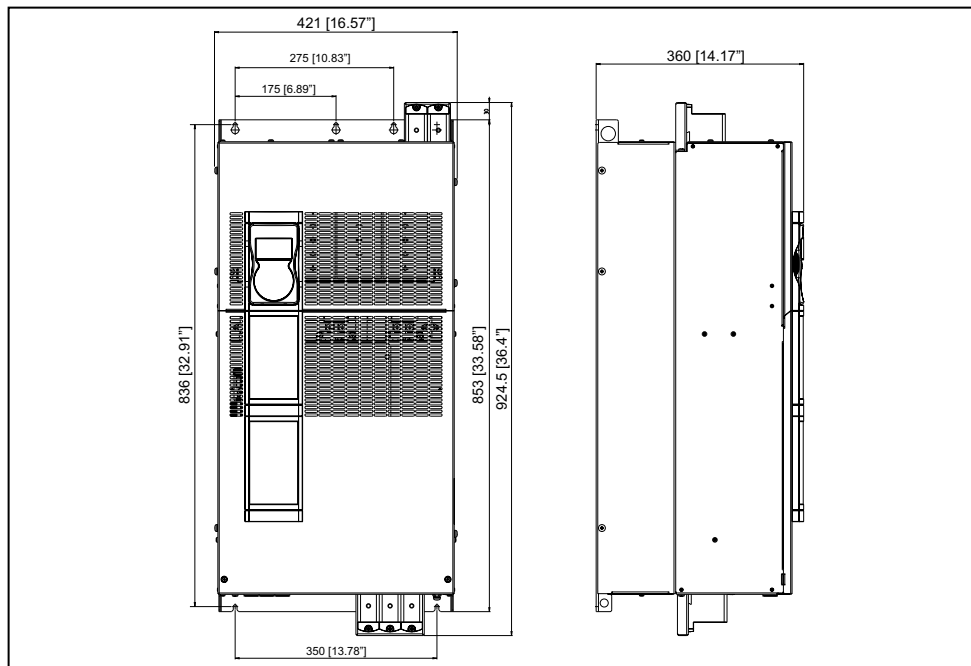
Размеры для типоразмера ADV61320...-DC
